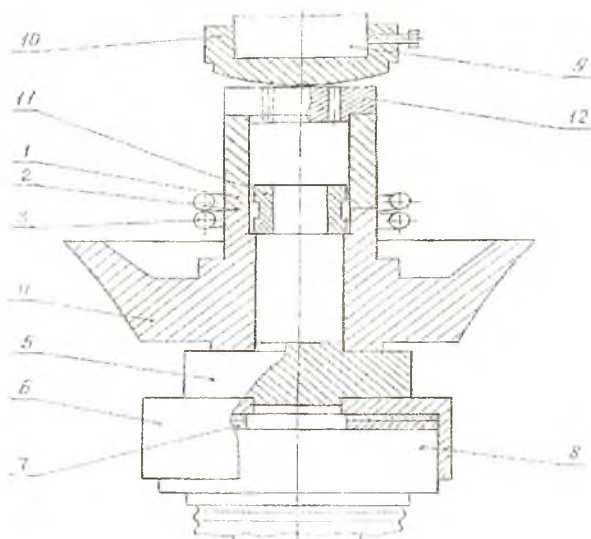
Оснастка для диффузионной сварки деталей биметаллических роторов компрессоров: 1 – втулка лабиринтного уплотнения, 2 – сварной стык, 3 – индуктор, 4 – рабочее колесо, 5 – подставка, 6 – центрирующий стакан, 7 – регулировочные прокладки, 8 – шток силового привода, 9 – упор вакуумной камеры, 10 – сферическая пята, 11 – технологическая центрирующая втулка, 12 – сухарь
